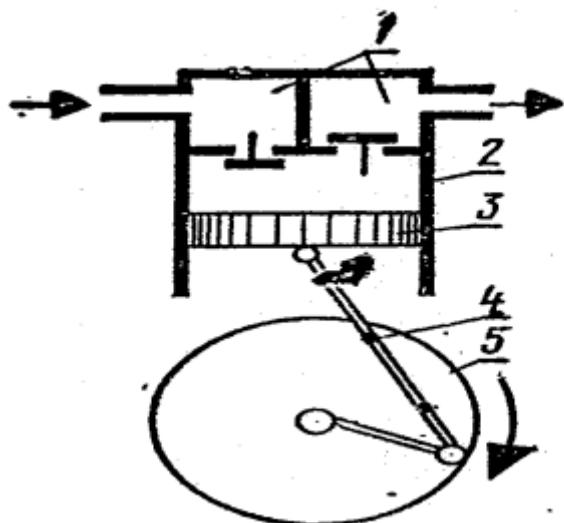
Схема работы поршневого компрессора: 1 – клапаны, 2 – цилиндр, 3 – поршень, 4 – шатунно-кривошипный механизм, 5 - маховик
